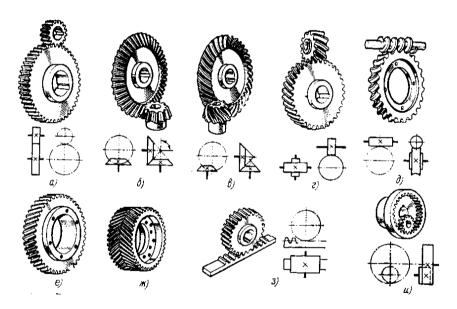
Виды зубчатых передач и их элементы: а – цилиндрическая; б – коническая; в – гипоидная; г – винтовая; д – червячная; е – косозубое зубчатое колесо; ж – шевронное зубчатое колесо; з – реечная; и – с внутренним зацеплением
